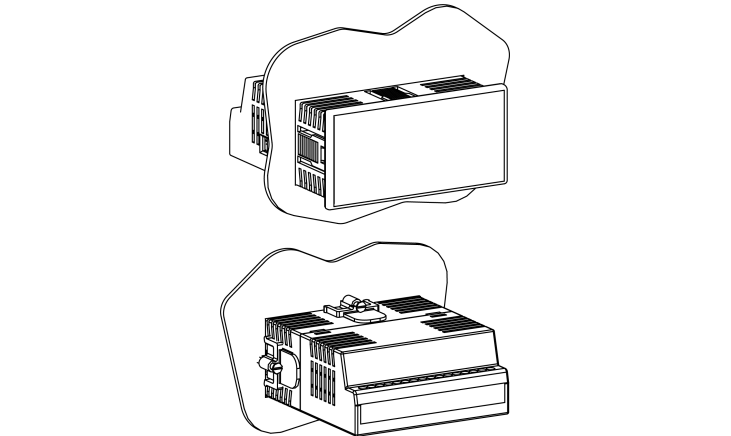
Монтаж прибора щитового крепления Щ2
